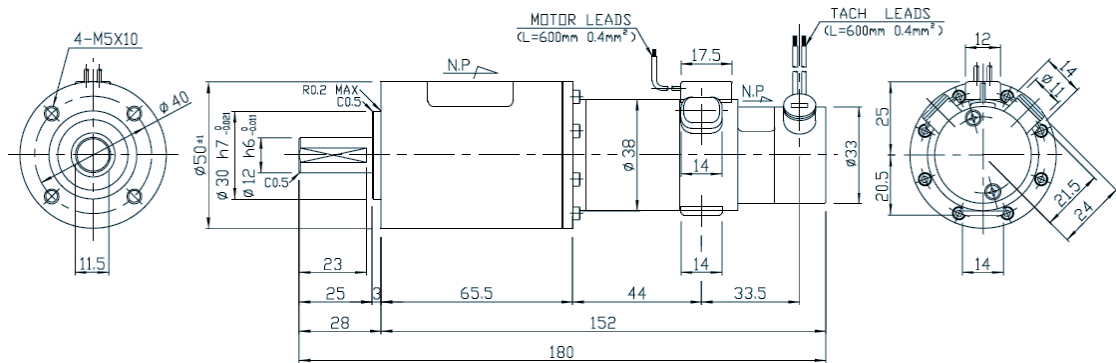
Dimensiones del motor con el tacómetro acoplado
